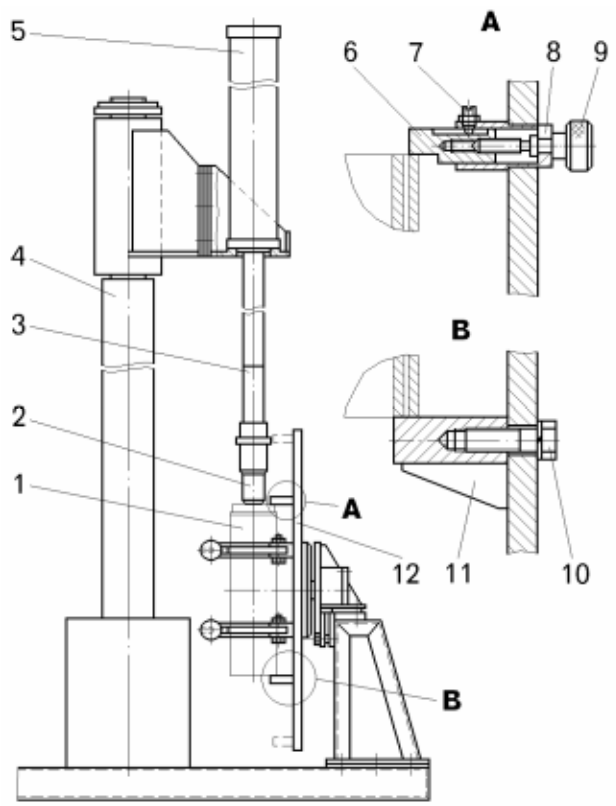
Стенд для сборки цилиндра опрокидывающего механизма:
